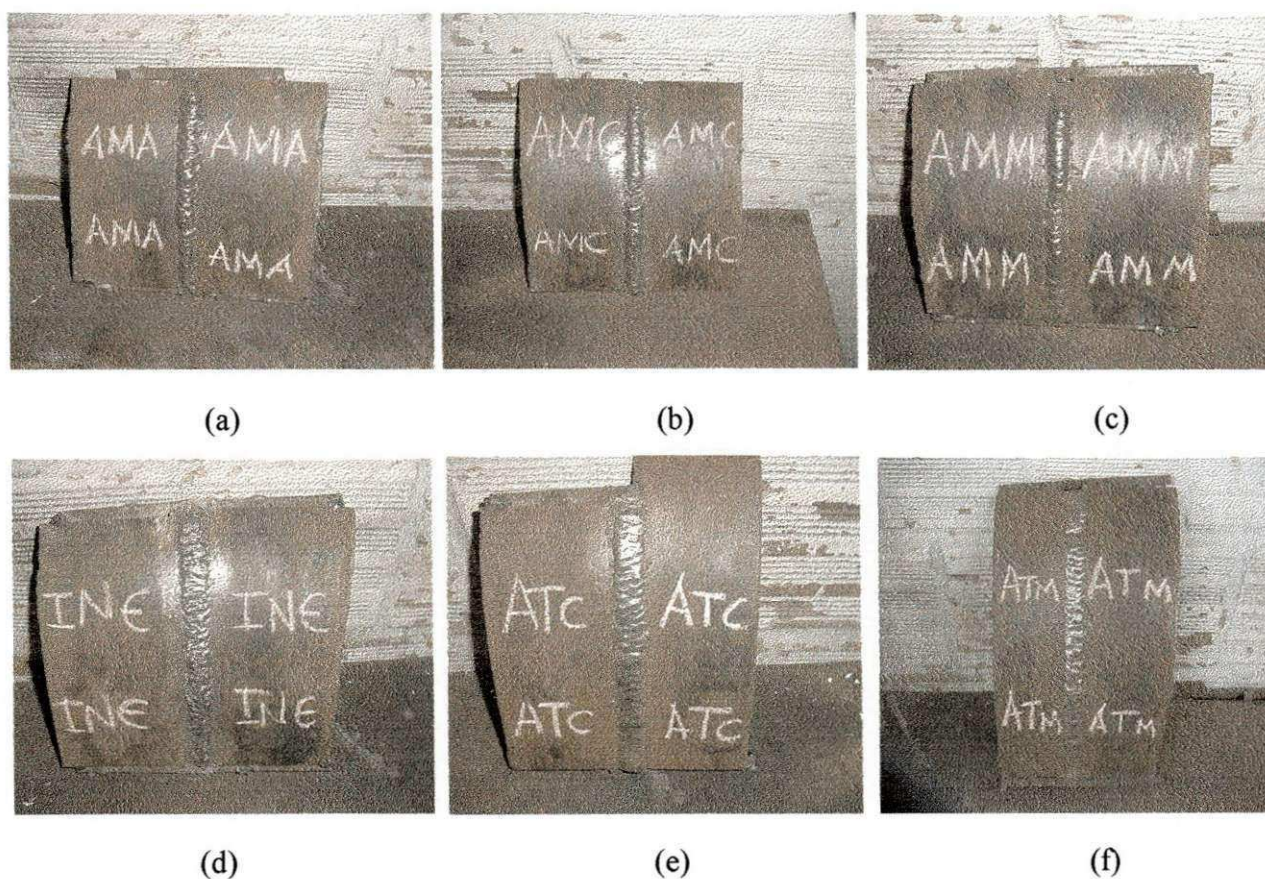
(a) Junta soldada para o processo MIG com proteção gasosa de argônio, (b) Junta soldada para o processo MAG com proteção gasosa de CO_2 , (c) Junta soldada para o processo MAG com proteção gasosa de mistura com 25% de CO_2 , (d) Junta soldada para o processo SAT sem proteção gasosa, (e) Junta soldada para o processo SAT com proteção gasosa de CO_2 e (f) Junta soldada para o processo SAT com proteção gasosa de mistura com 25% de CO_2 .
